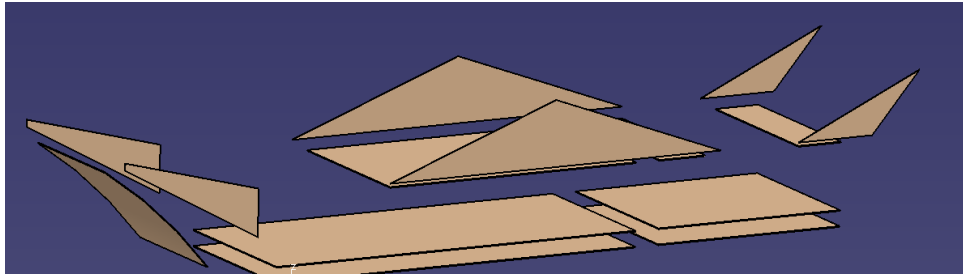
, Conjunto de láminas que irán soldadas al chasis
